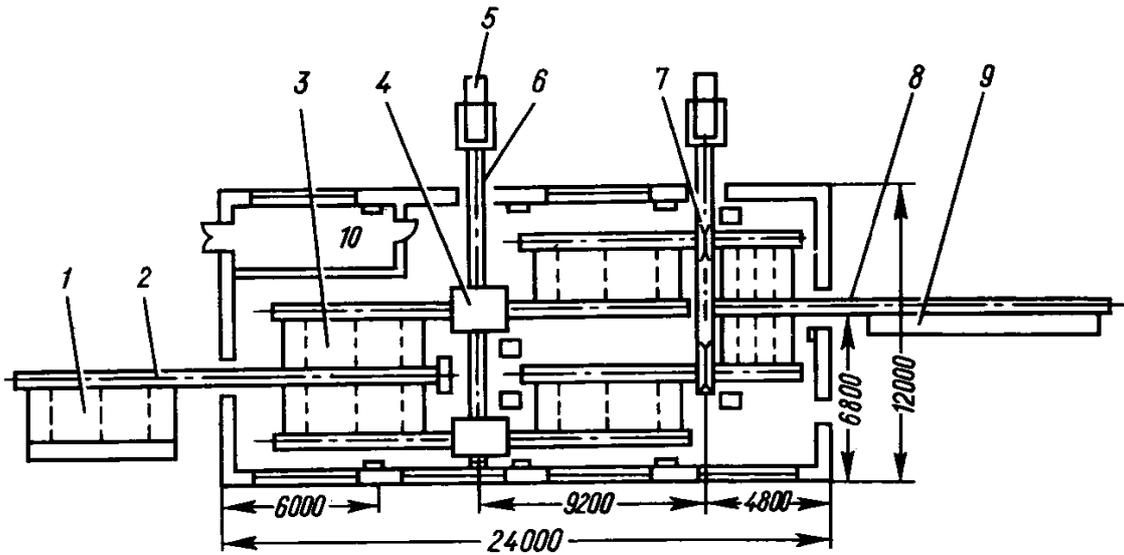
Технологическая схема рудстоечно-балансового цеха: 1 – бункерный питатель; 2 – подающий лесотранспортер; 3 – поперечный лесотранспортер; 4 – окорочный станок; 5 – скиповый погрузчик ЛВ-175; 6 – лесотранспортер отходов; 7 – пила АЦ-3С; 8 – лесотранспортер для выноса готовой продукции; 9 – накопитель; 10 – отделение для обслуживания дереворежущего инструмента
